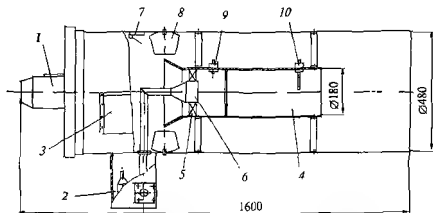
Газовый воздухонагреватель ГЦ-70
